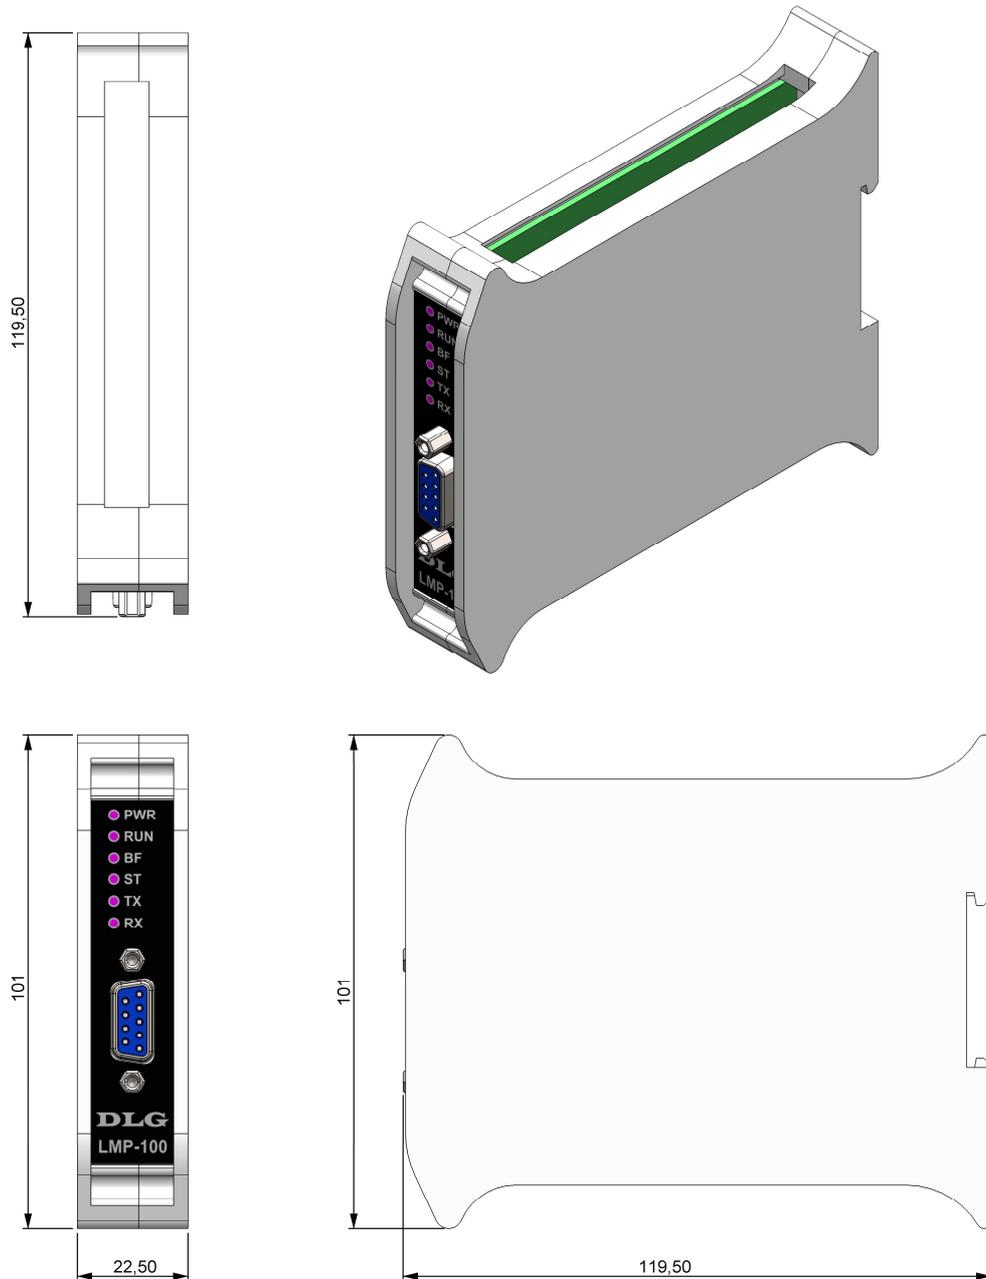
Dimensionamento para montagem (cotas em milímetros)
